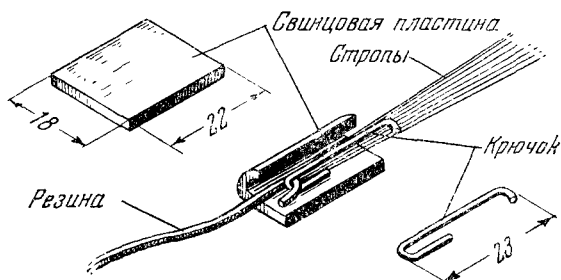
Закрепление строп, крючка и резины в свинцовой пластине
